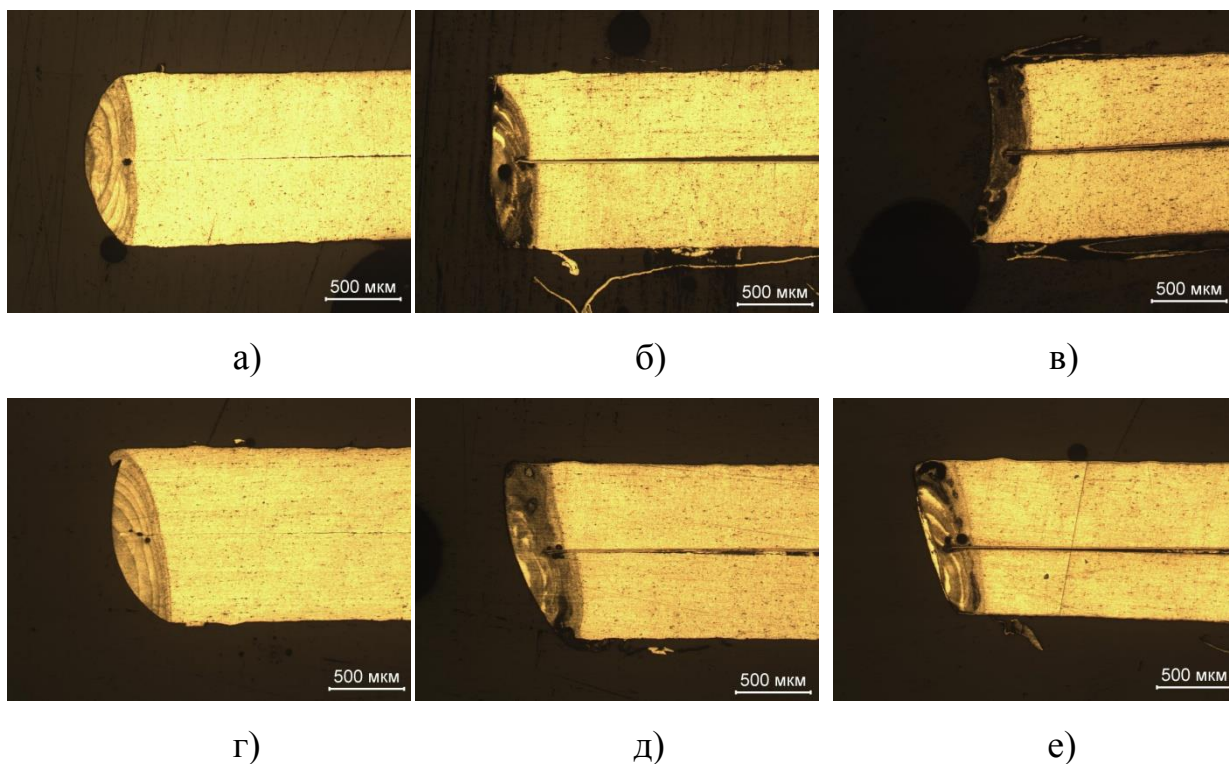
Макроструктура сварных соединений:
